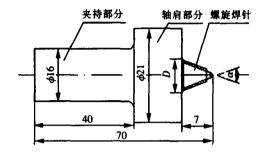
螺旋形搅拌头外形示意图 Fig. 1 Scheme of rotating tool
